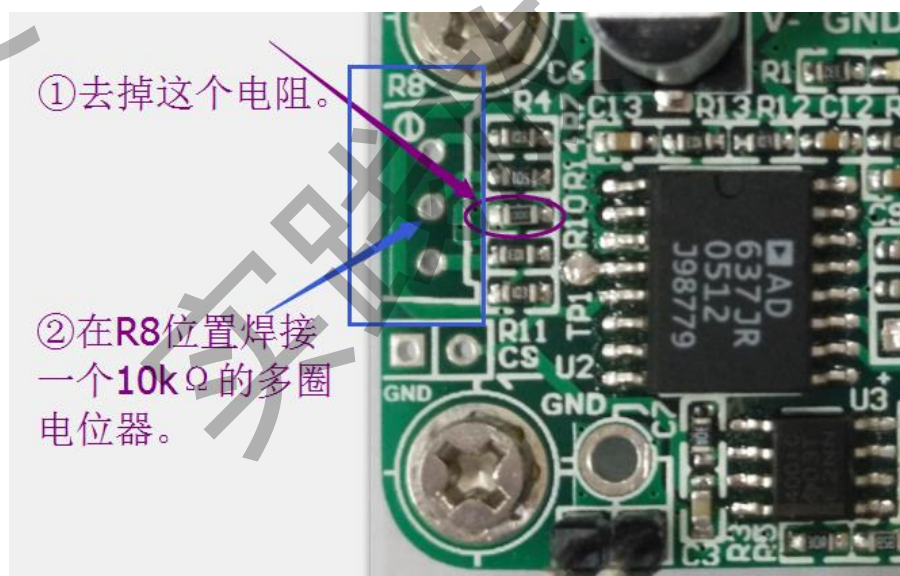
焊接输出有效值校准电位器 R8 的方法
